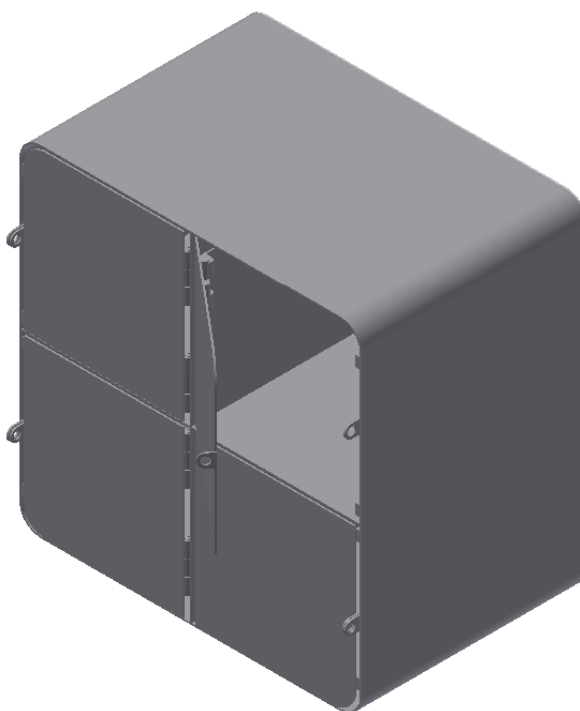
Zadní pohled na zaparkovaná kola
